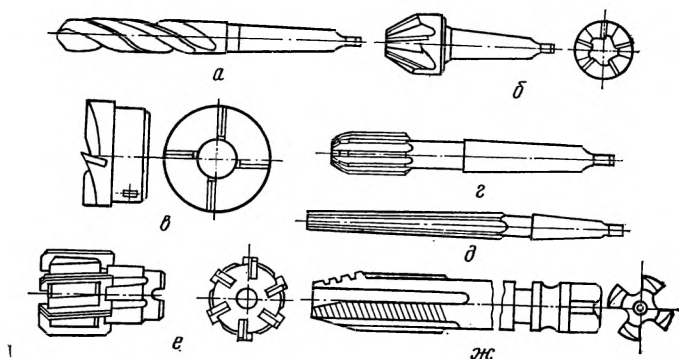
Инструменты для обработки отверстий на сверлильных станках
